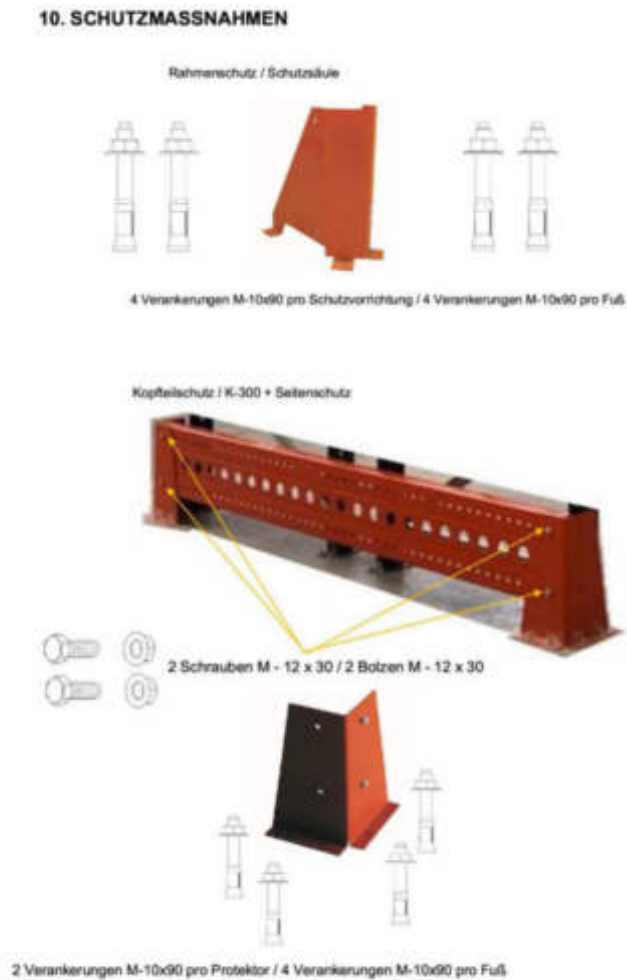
Protection de cadre et protection d'extrémité (K-300 + protection latérale) avec quincaillerie.
